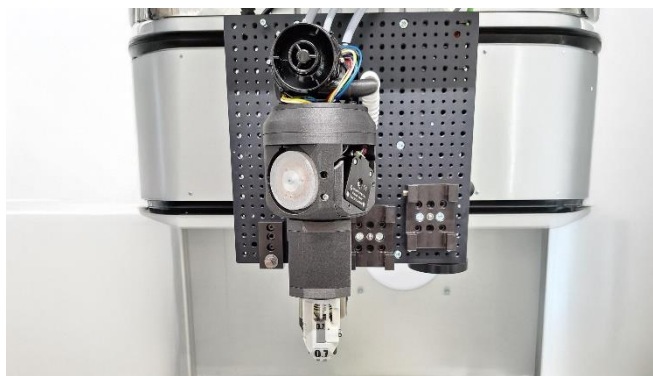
WEAM Machine*, gekoppelt mit einer Werkzeugmaschine.
